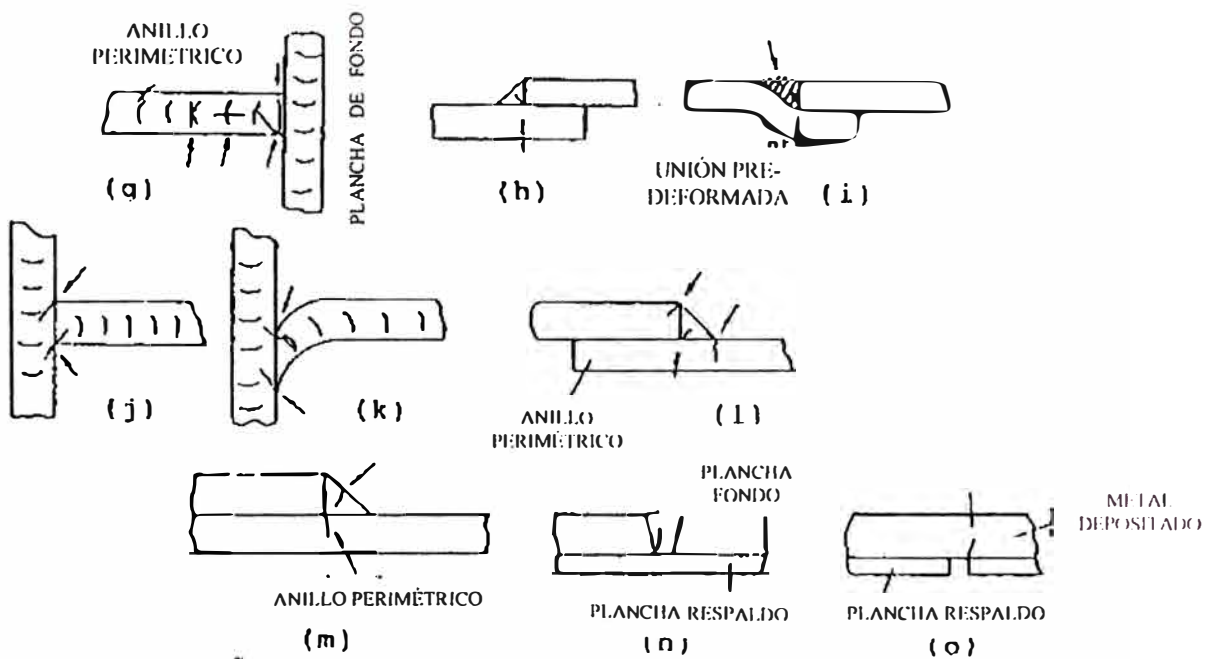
Fisuras de juntas de anillo perimétrico y planchas de fondo.
